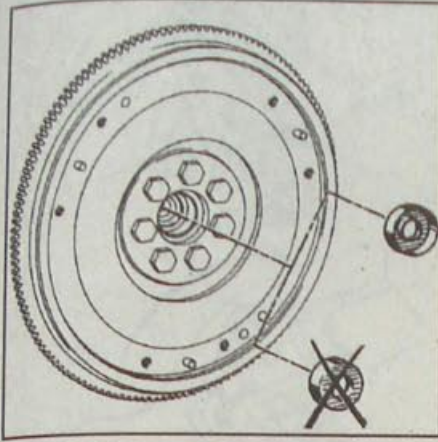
Направление установки втулки в торце коленчатого вала
